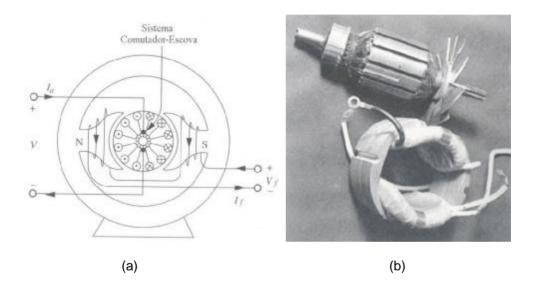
Desenho (a) e foto (b) de um motor CC de 2 pólos
